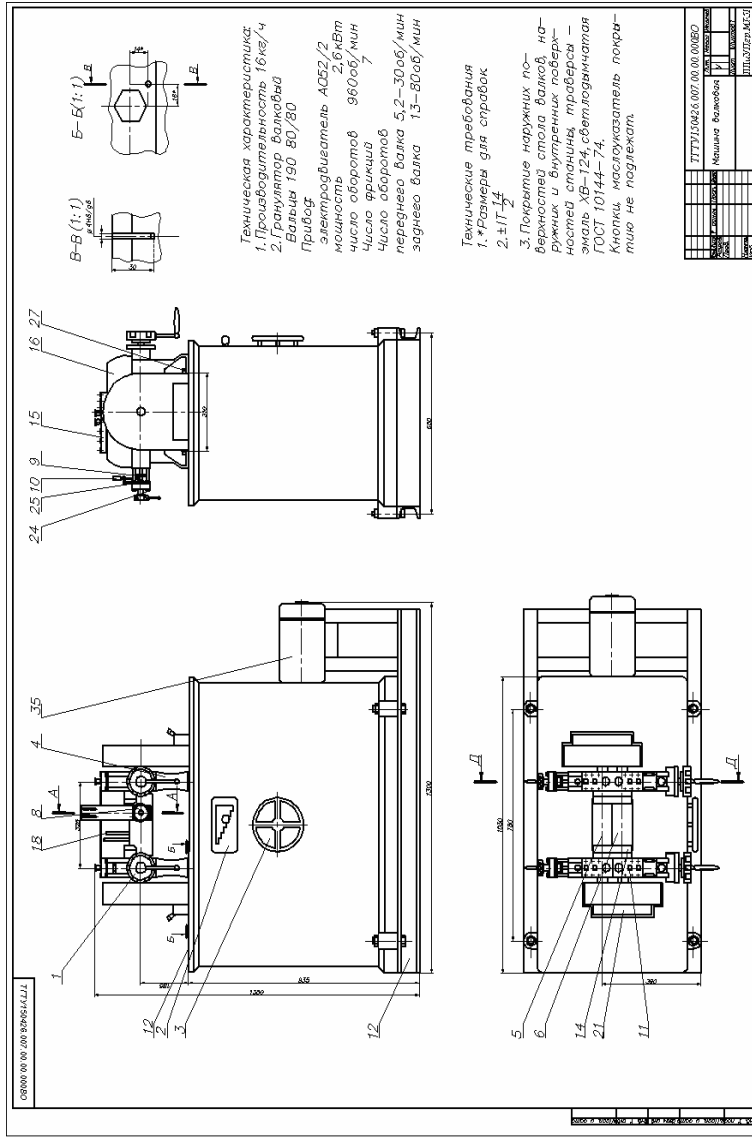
Чертеж общего вида валкового пластилятора-гранулятора (лист 1)
